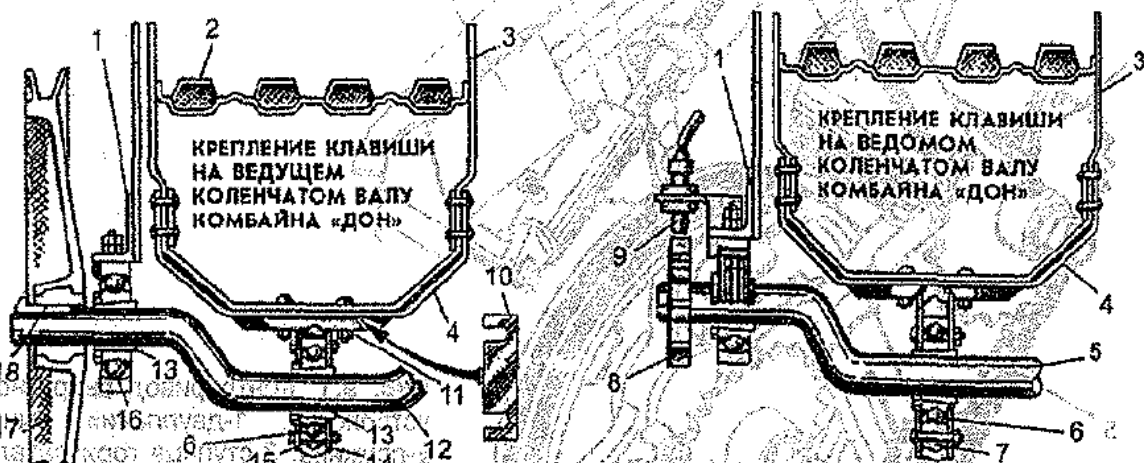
Крепление клавиш на валах: 1 - кронштейн; 2 - жалюзийная поверхность; 3 - корпус клавиши; 4 - кронштейн; 5 - ведомый коленчатый вал; 6, 16 - подшипники; 7 - кольцо; 8 - звездочка; 9 - датчик; 10 - прокладка; 11 - корпус подшипника; 12 - ведущий коленчатый вал; 13 - конусная втулка; 14, 15 - шайбы; 17 - шкив; 18 - шпонка
